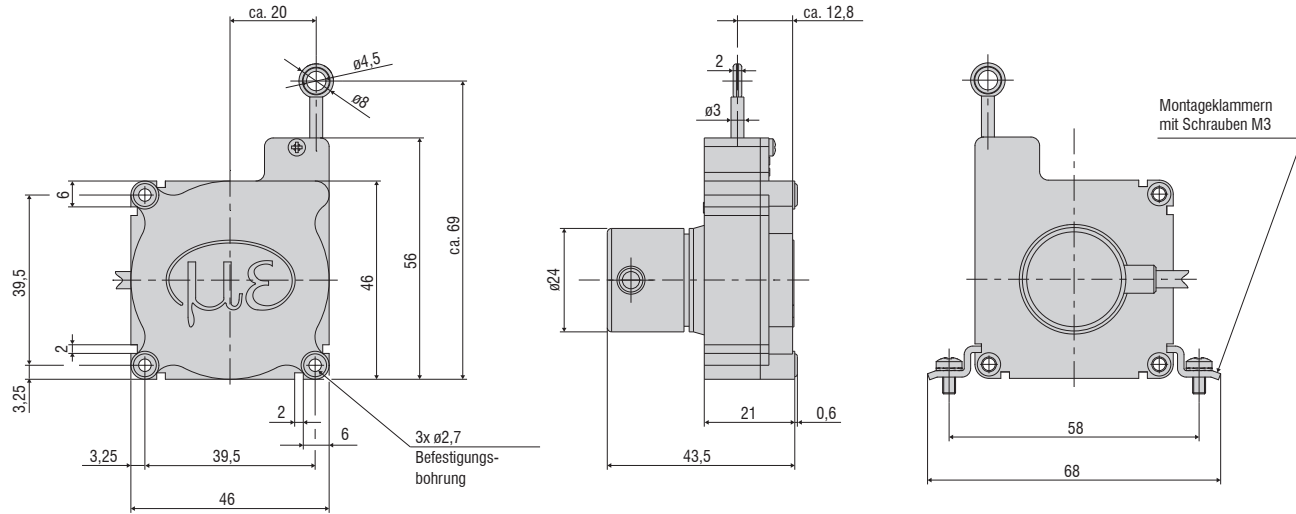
Maßzeichnung WPS-xxx-MK46-Exxx mit Encoder, Abmessungen in mm
